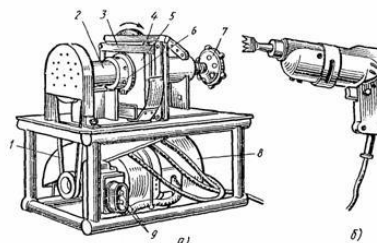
Переносный станок (а) для высверливания отверстий и ручная сверлильная машина (б) с насадкой: 1 - клиноременная передача, 2 - корпус подшипника рабочего вала, 3 - рамка, 4 - стопорный рычаг, 5 - плитка, 6 - резцедержатель, 7 - механизм горизонтальной подачи плитки, 8 - электродвигатель, 9 - кнопки управления
